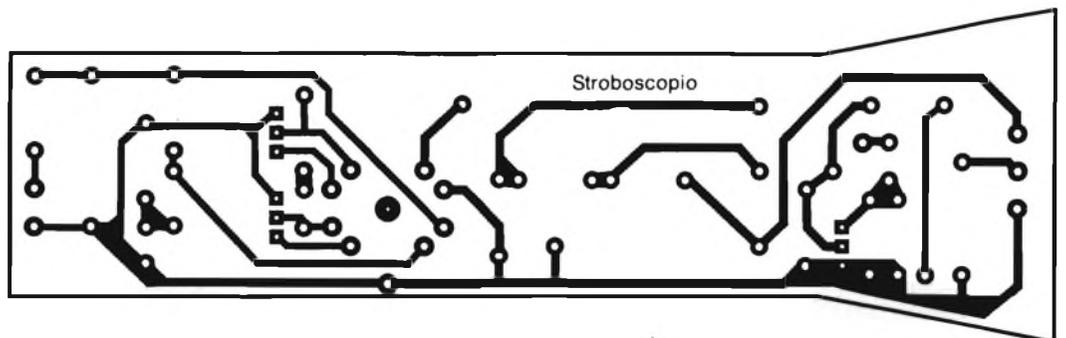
Circuito stampato dello stroboscopio lampeggiatore. Le sue dimensioni permettono di inserirlo in un astuccio per lampada tascabile (vedi testo).
